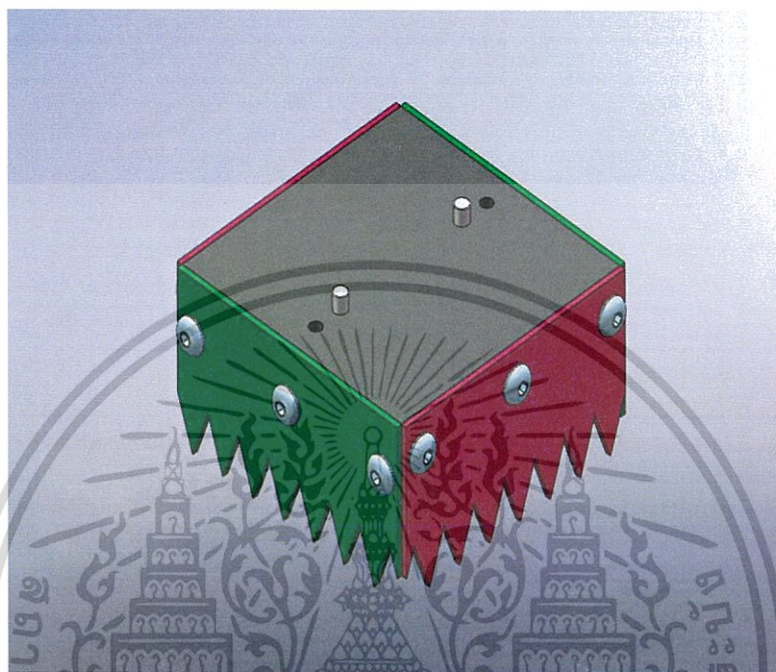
(แสดงตัวอย่างของ Drawing ตัว Part Cutter A)
